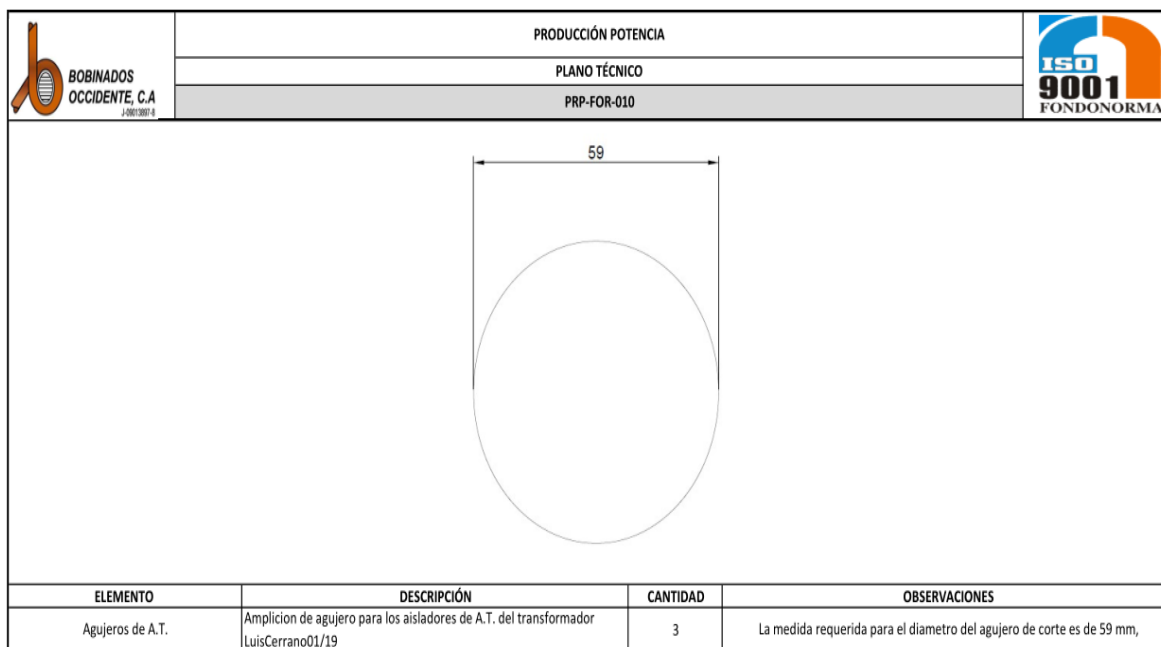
PRP-FOR-010 PLANO TÉCNICO (Plano para corte de adecuación de aisladores de A.T.).
